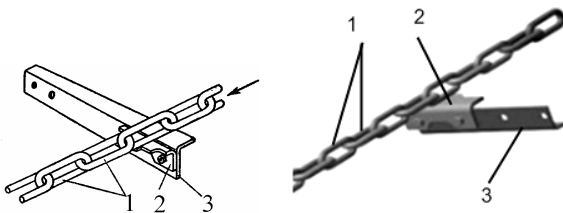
Цепь со скребками транспортера ТСН-160А:
